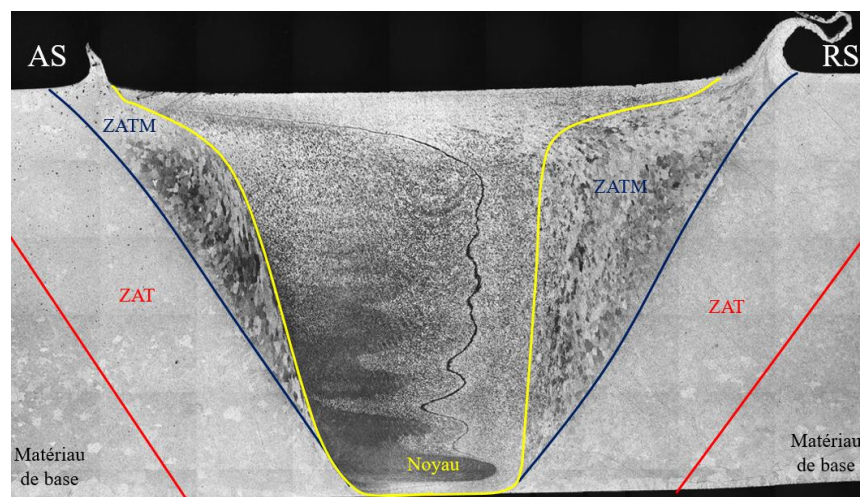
Macrostructure d'une soudure d'alliage 6061-T6 de 9,53 mm
